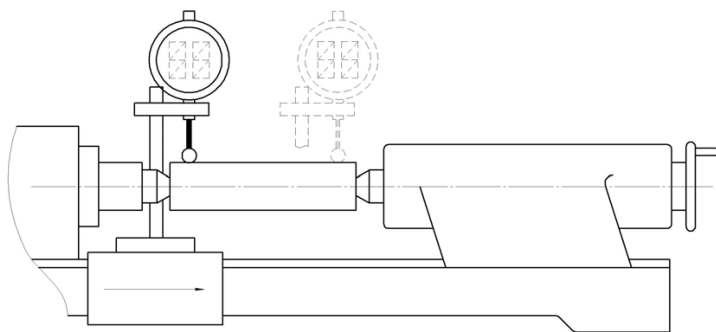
Схема установки индикатора для проверки расположения осей отверстий шпинделя передней бабки и пиноли на одинаковой высоте над направляющими станины для суппорта
